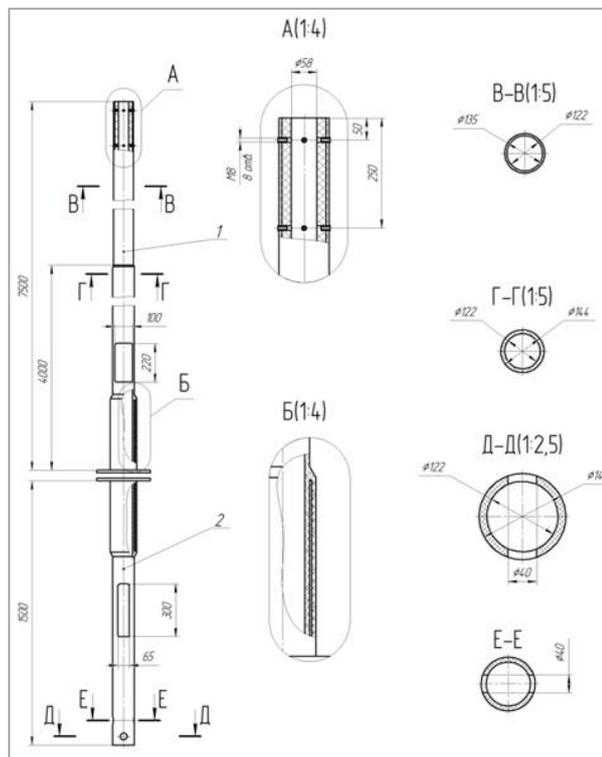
Сборный чертеж опоры ОГО-7,5-100-ф от ООО "Композит Групп"
